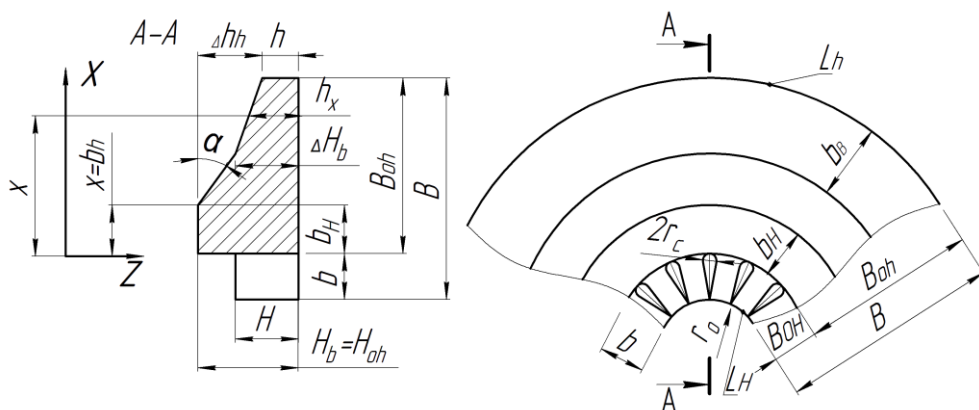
Розрахункова схема розгортки витка ГЗ із не вальцьованою зоною
